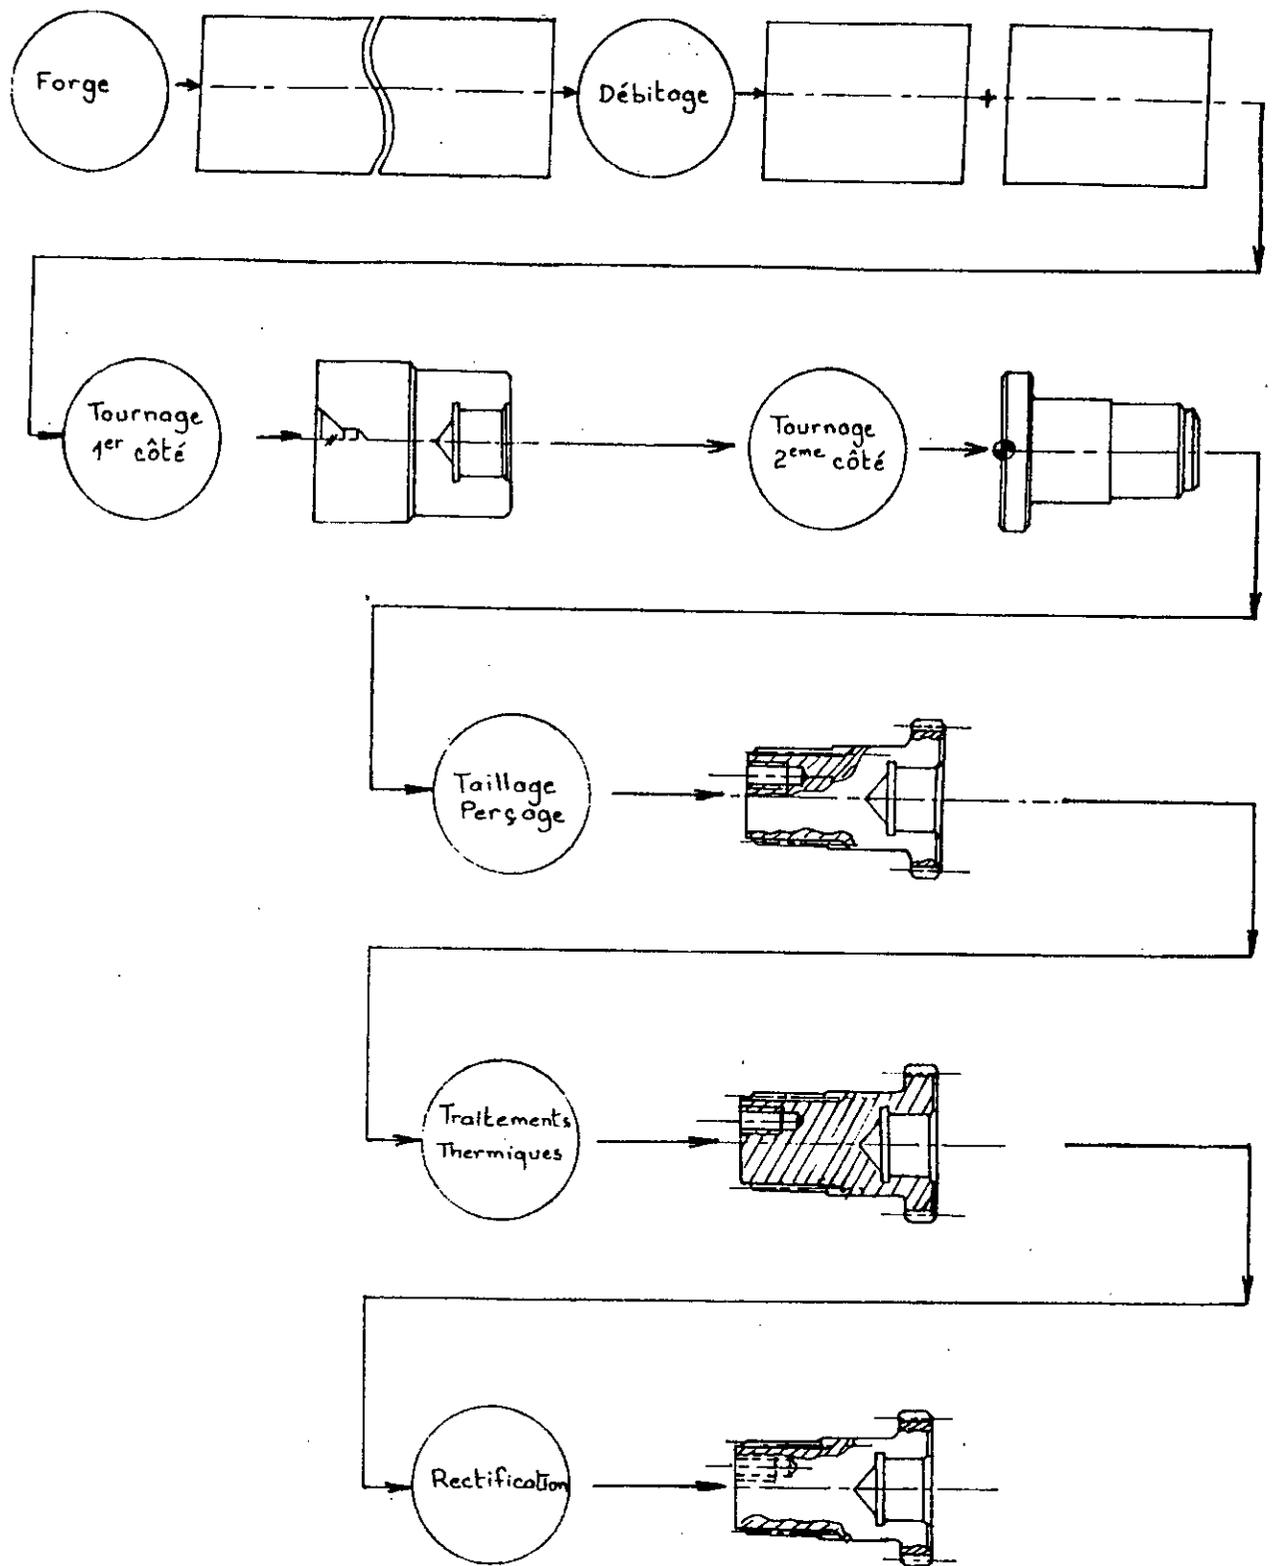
procédé de fabrication de l'arbre de sortie avant (166052).
